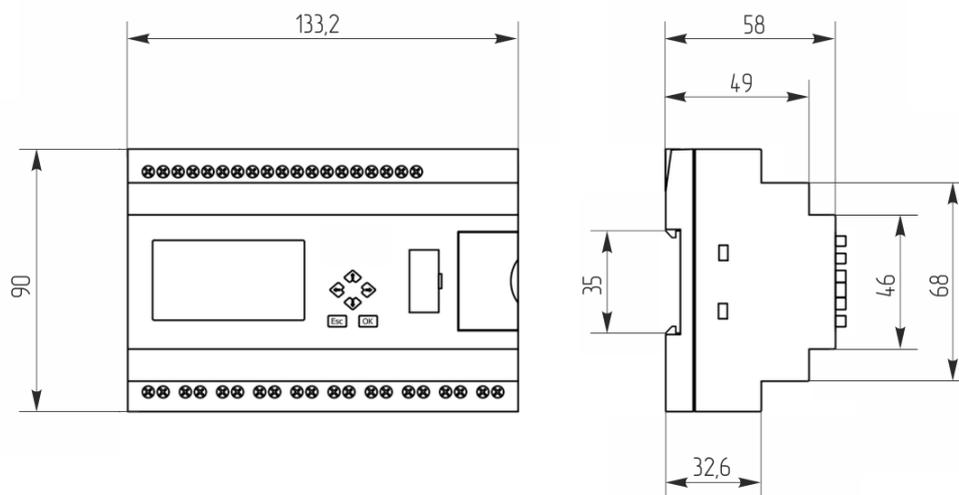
Габаритные и установочные размеры модуля ЦПУ
